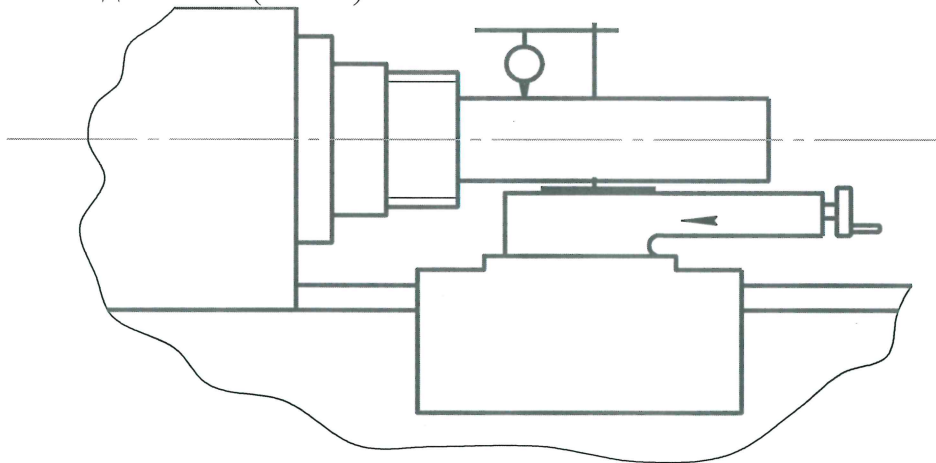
Схема установки индикатора для проверки параллельности направления перемещения салазок суппорта оси шпинделя
